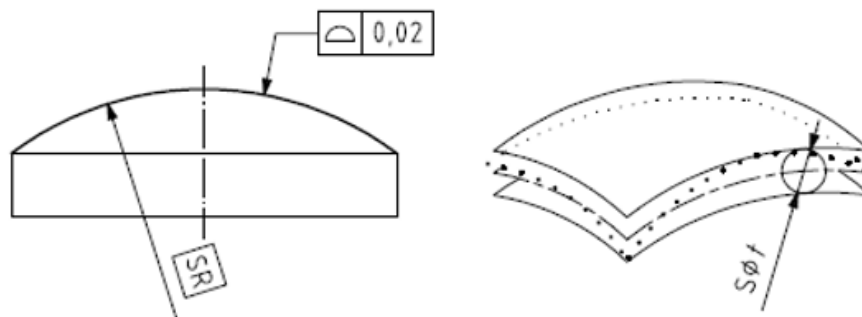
Tolerance tvaru profilu bez základny [2]
